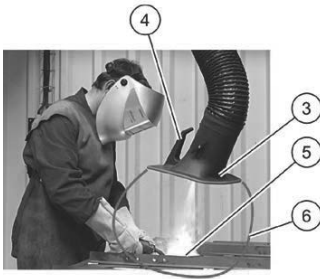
Отсос дыма, образующегося в процессе сварки
